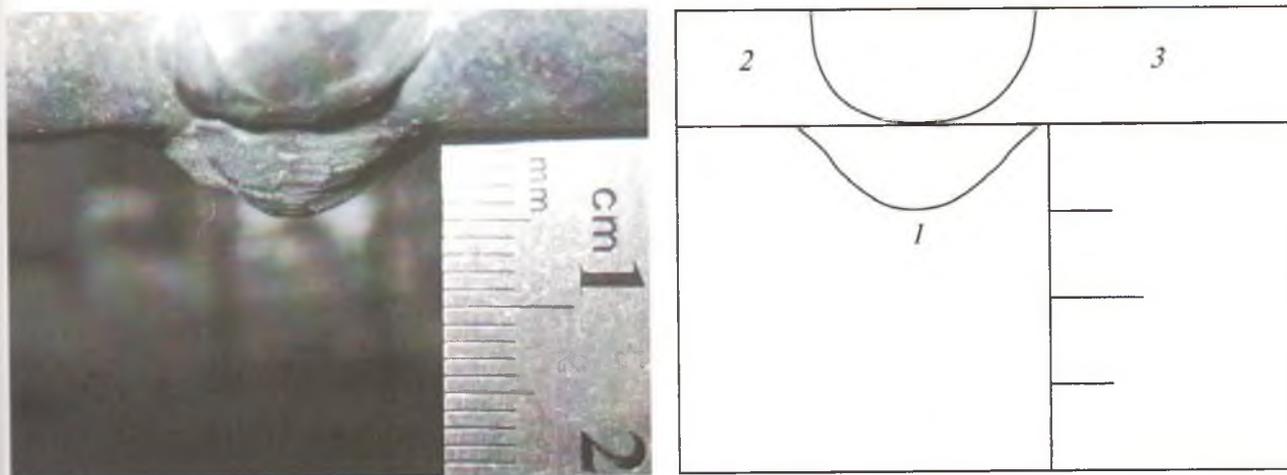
Выпуклость шва *1* – часть стыкового сварного шва, выступающая над уровнем поверхностей сваренных деталей *2* и *3*, в сварном соединении профиля квадратного сечения строительной конструкции. Вид вдоль оси шва
